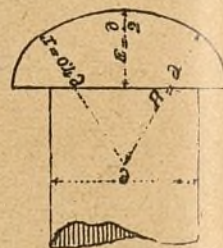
Roblón. Dimensiones según M. Guilford L. Molesworth.
